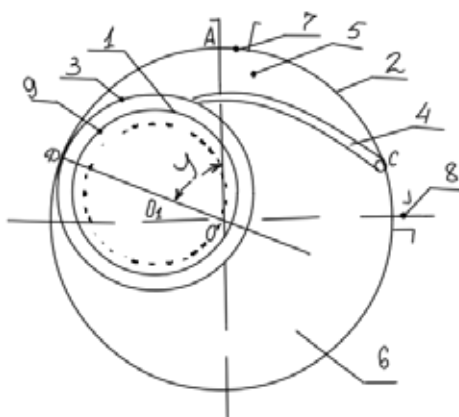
Принципова схема роботи пневматичного ротаційно-поршневого двигуна
